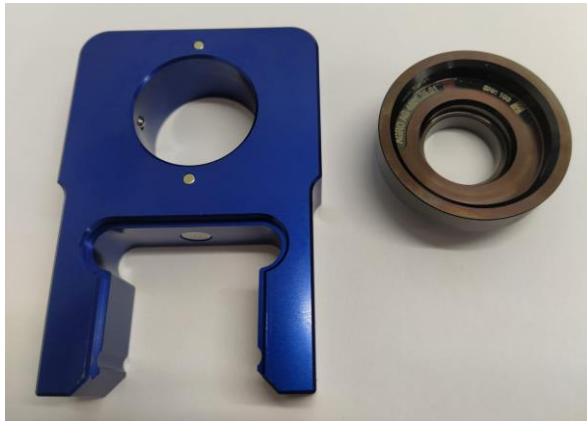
Attrezzo di serraggio e inserto di serraggio
